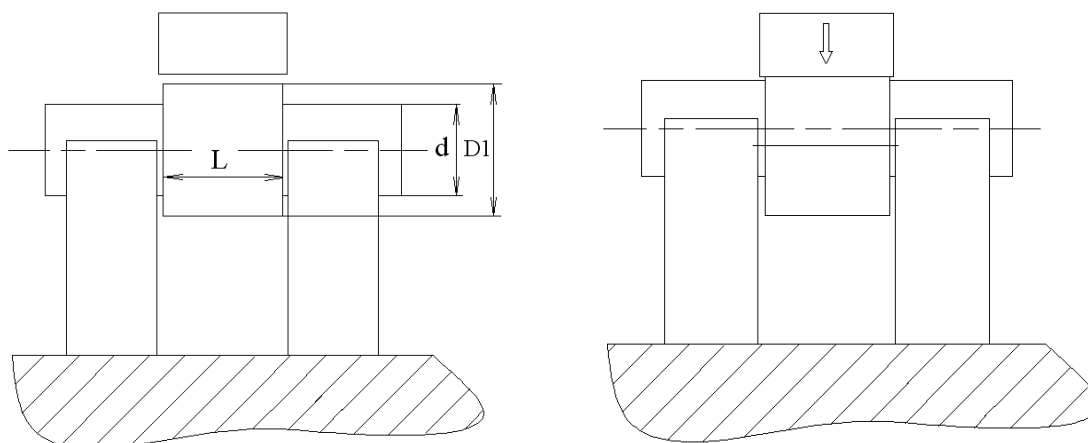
Ковка эксцентрикового вала смещением утолщения
